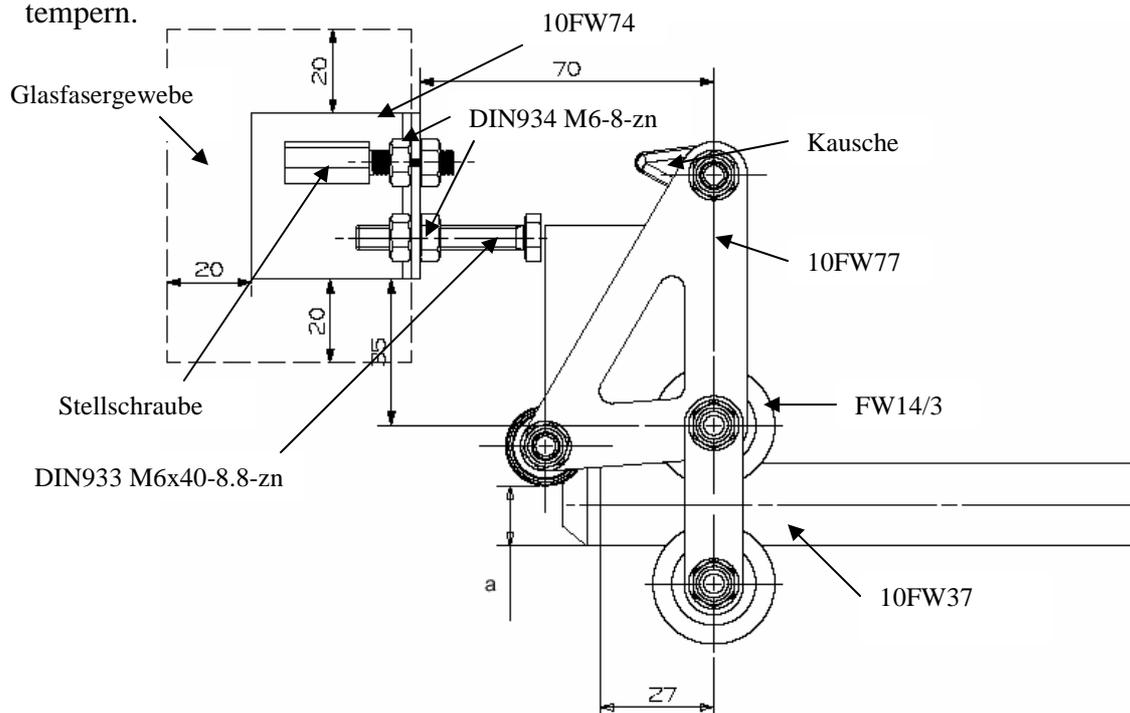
Einbau des Trägers für Anschlag und Bowdenzugeinstellung
